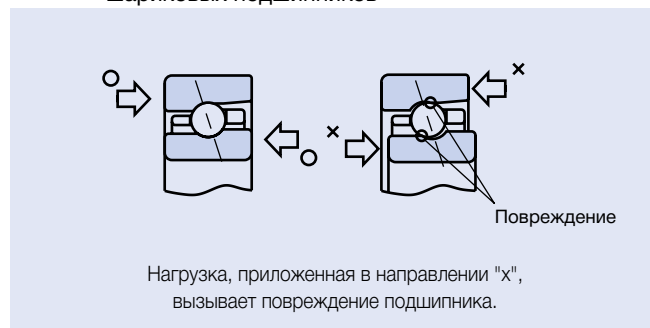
Монтаж компоновки "спина к спине" – 2 подшипника
